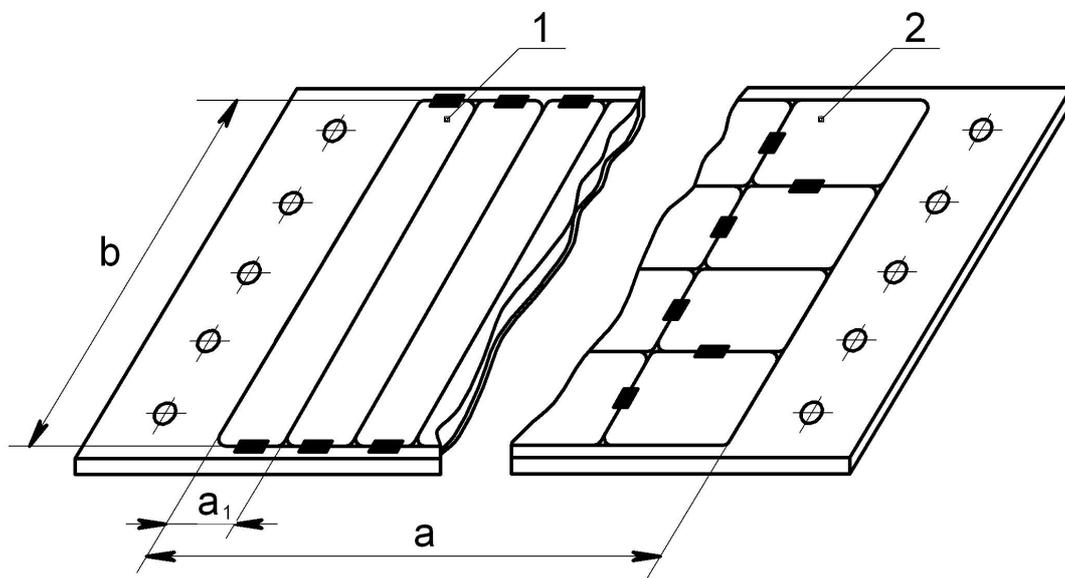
Нижняя часть формообразующей поверхности оснастки с нагревательным слоем: 1 – из пластин; 2 – блоков с сердечником
